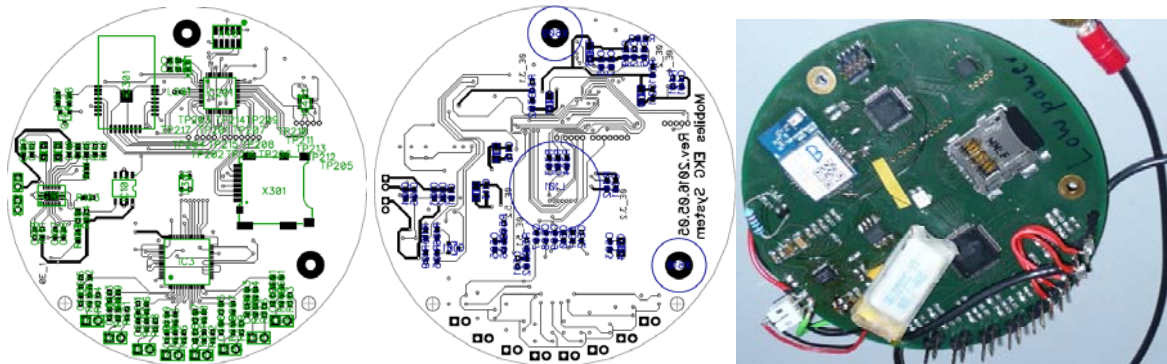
Realisierung des Prototyps des Recorders. Links: Layout und Placement TOP – Seite, Mitte: Layout und Placement BOTTOM Seite, Rechts: Prototyp mit Verbindung zu zwei externen Elektroden.
